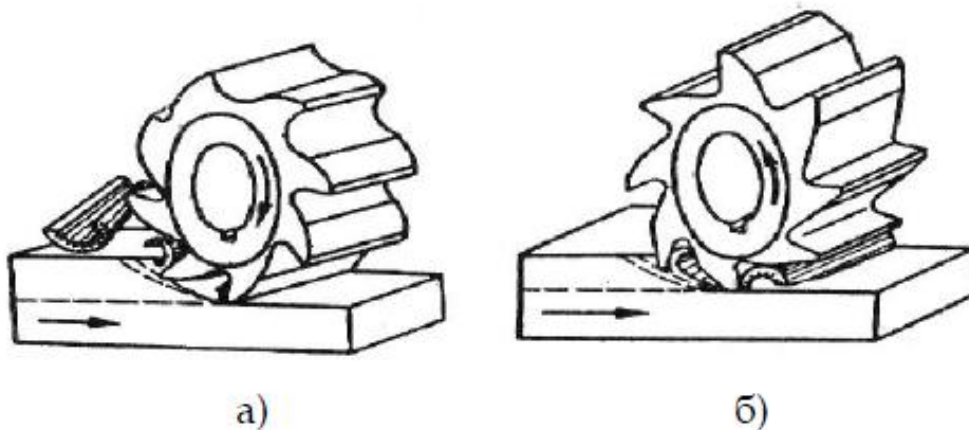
Фрезерування площини циліндричною фрезою: а – проти подачі; б – за подачею
